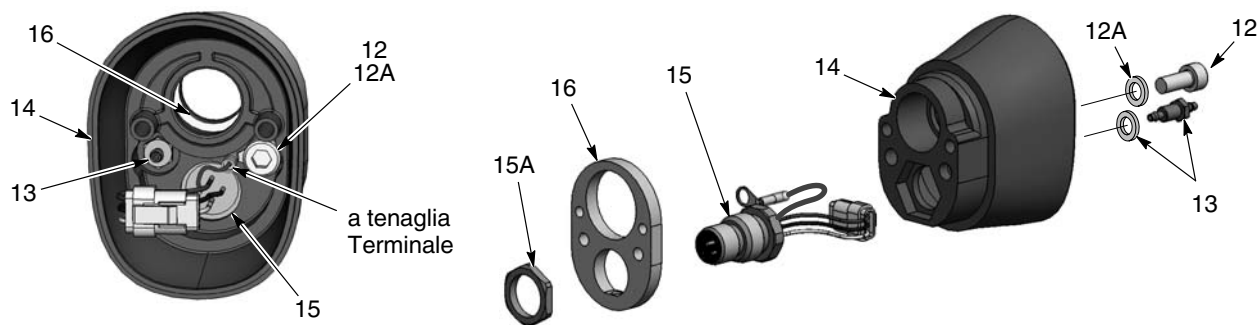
Smontaggio della pistola con montaggio su tubo 5 di 5
